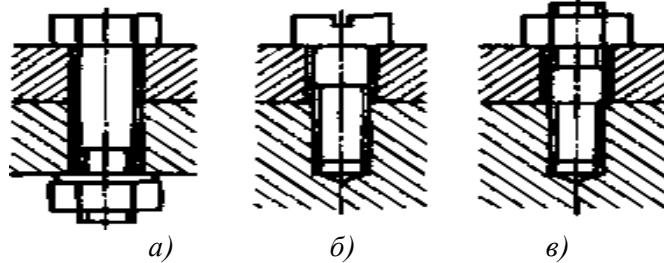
Основные крепежные детали резьбовых соединений:
